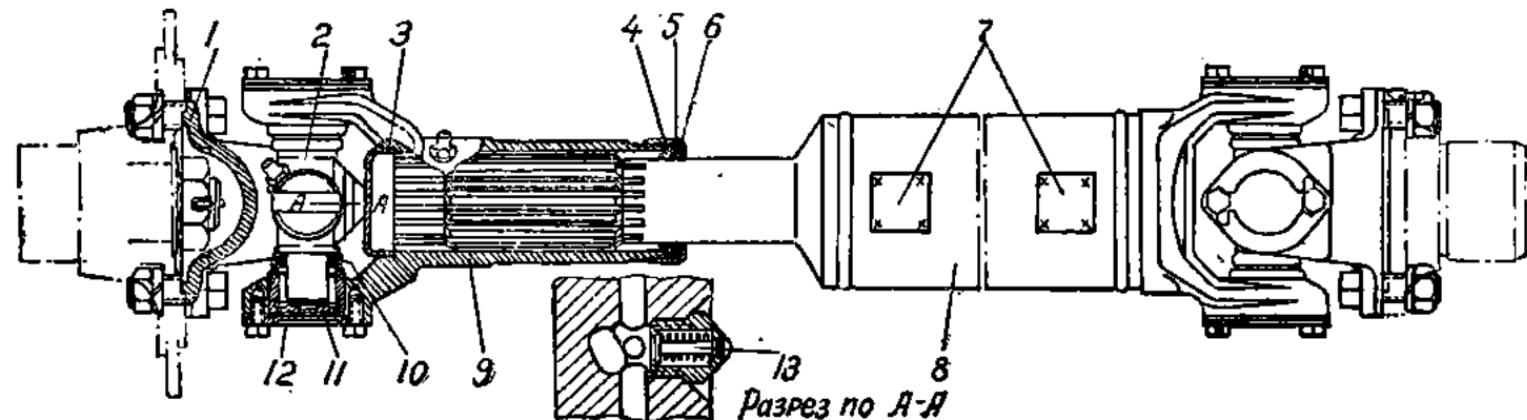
Карданный вал. (1 — вилка; 2 — крестовина; 4, 5 и 6 — детали сальника; 7 — балансировочные пластины; 8 — труба вала; 9 — скользящая вилка; 10 — сальник; 11 — игольчатый подшипник; 12 — крышка подшипника; 13 — предохранительный клапан (против чрезмерного повышения давления смазки)).
